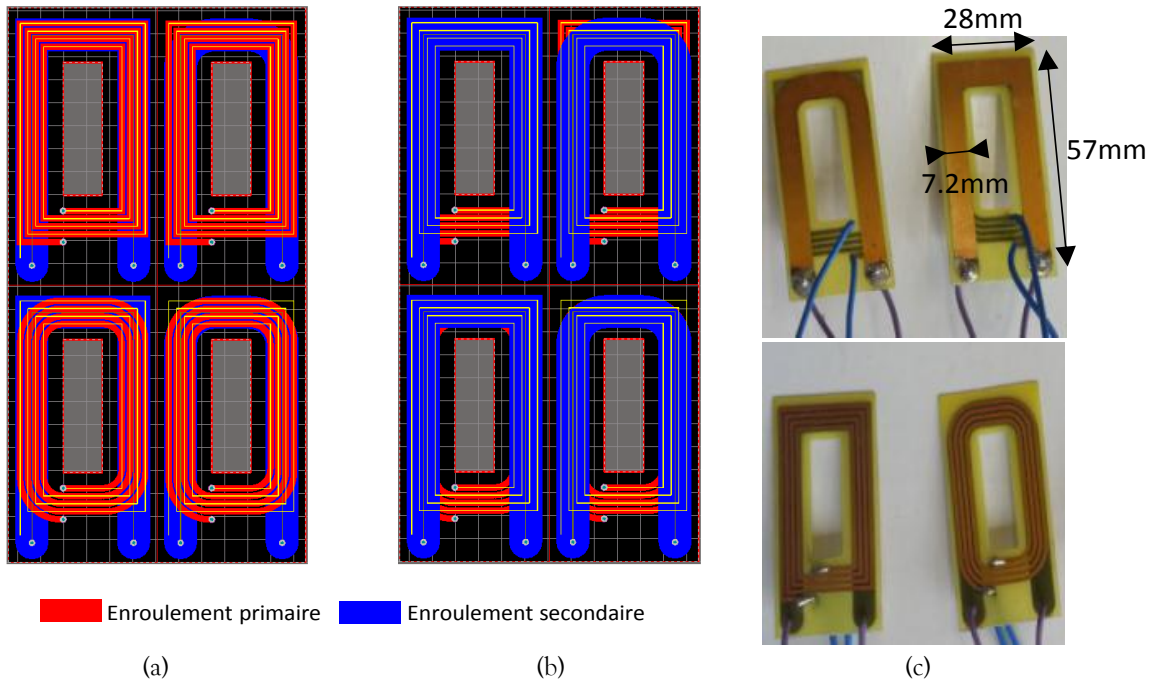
PCB réalisés : (a) CAO vue de dessus, (b) CAO vue de dessous et (c) prototypes
